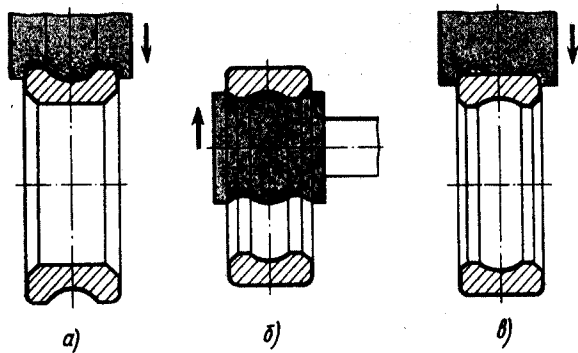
Схема врезного профильного шлифования внутреннего (а) и наружного (б, в) колец шарикоподшипника кругами, рабочая поверхность которых правится алмазными роликами
